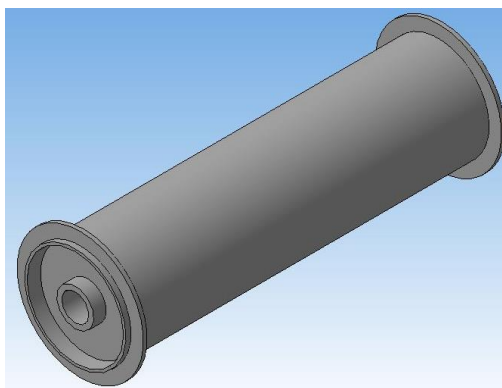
Сварной барабан лебёдки БК410
